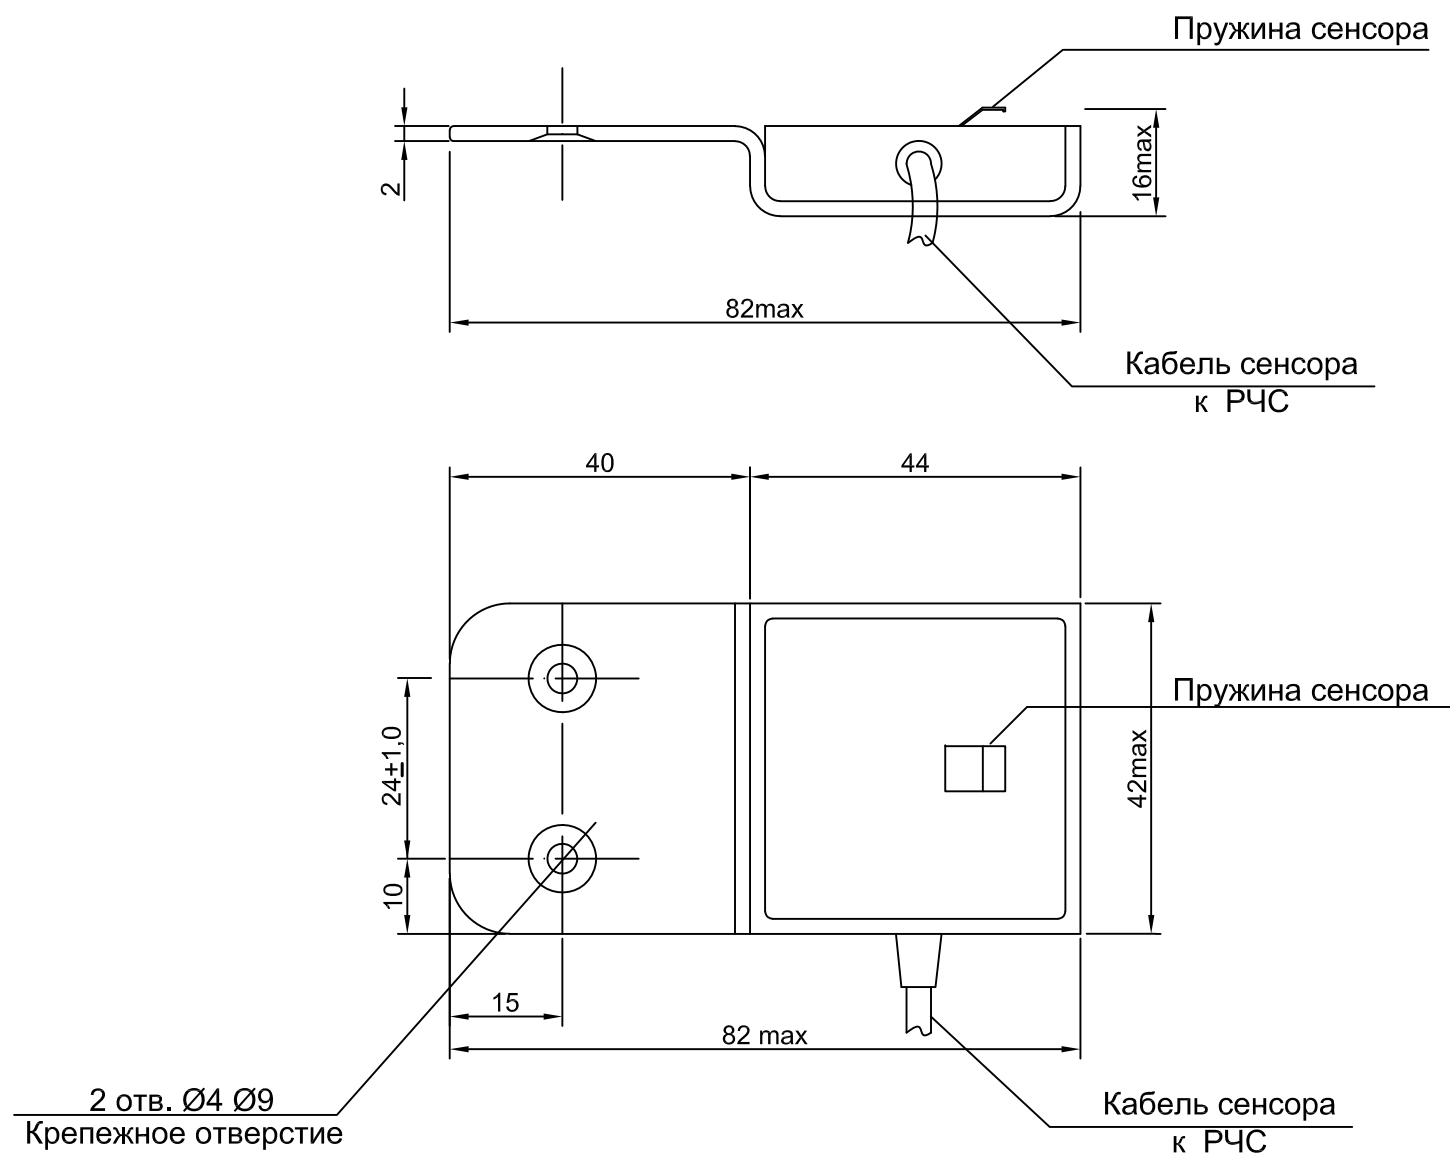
Габаритные размеры сенсора СПП-1Г2 с узлом крепления
